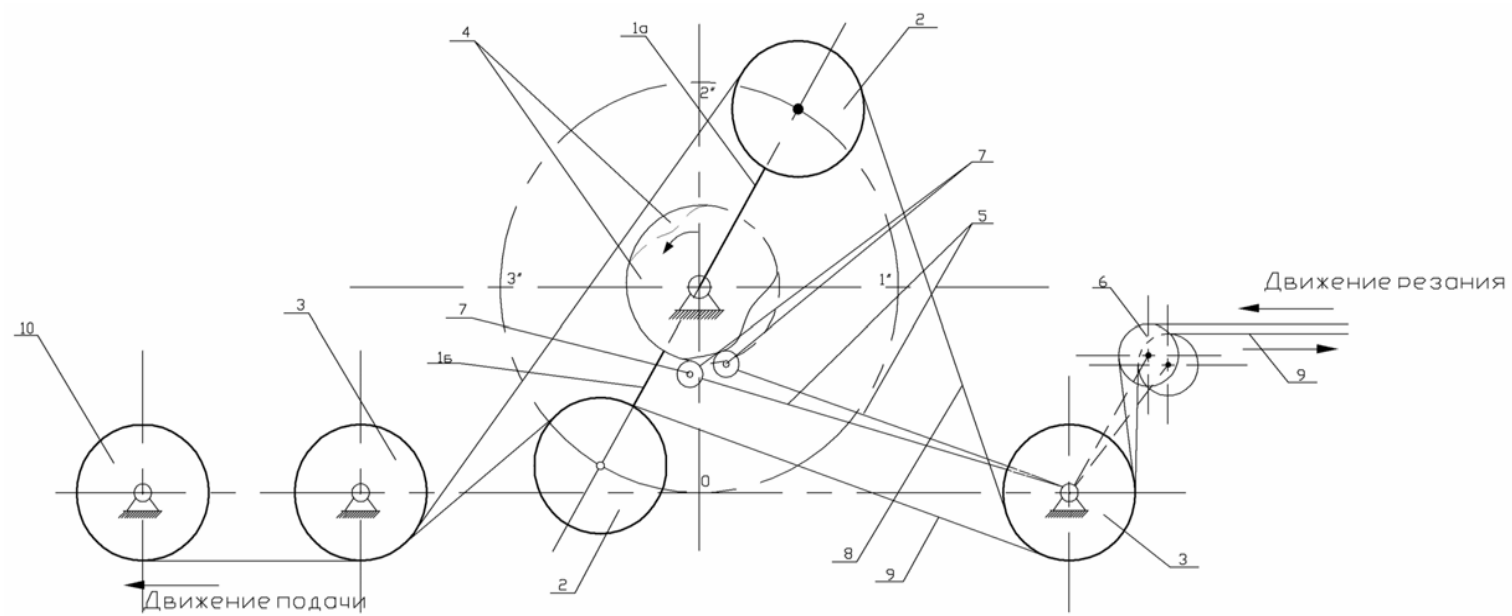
Структурная схема рычажно-роликового реверсора привода пилы типа ПП
